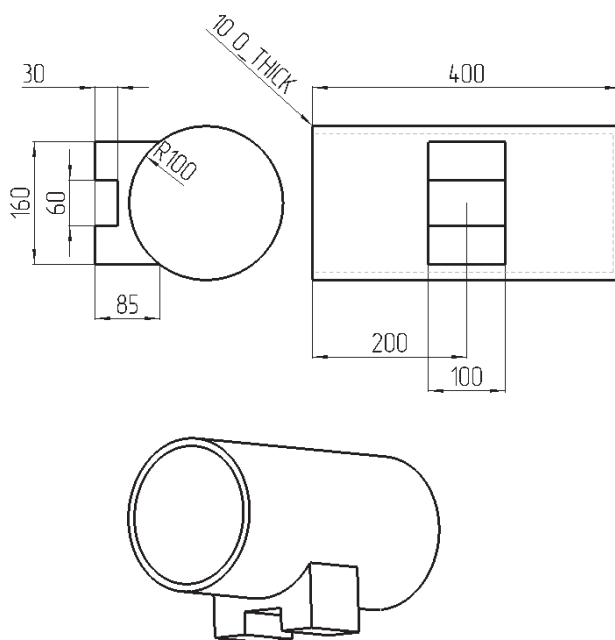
Общий вид и габаритные размеры модели оболочки
